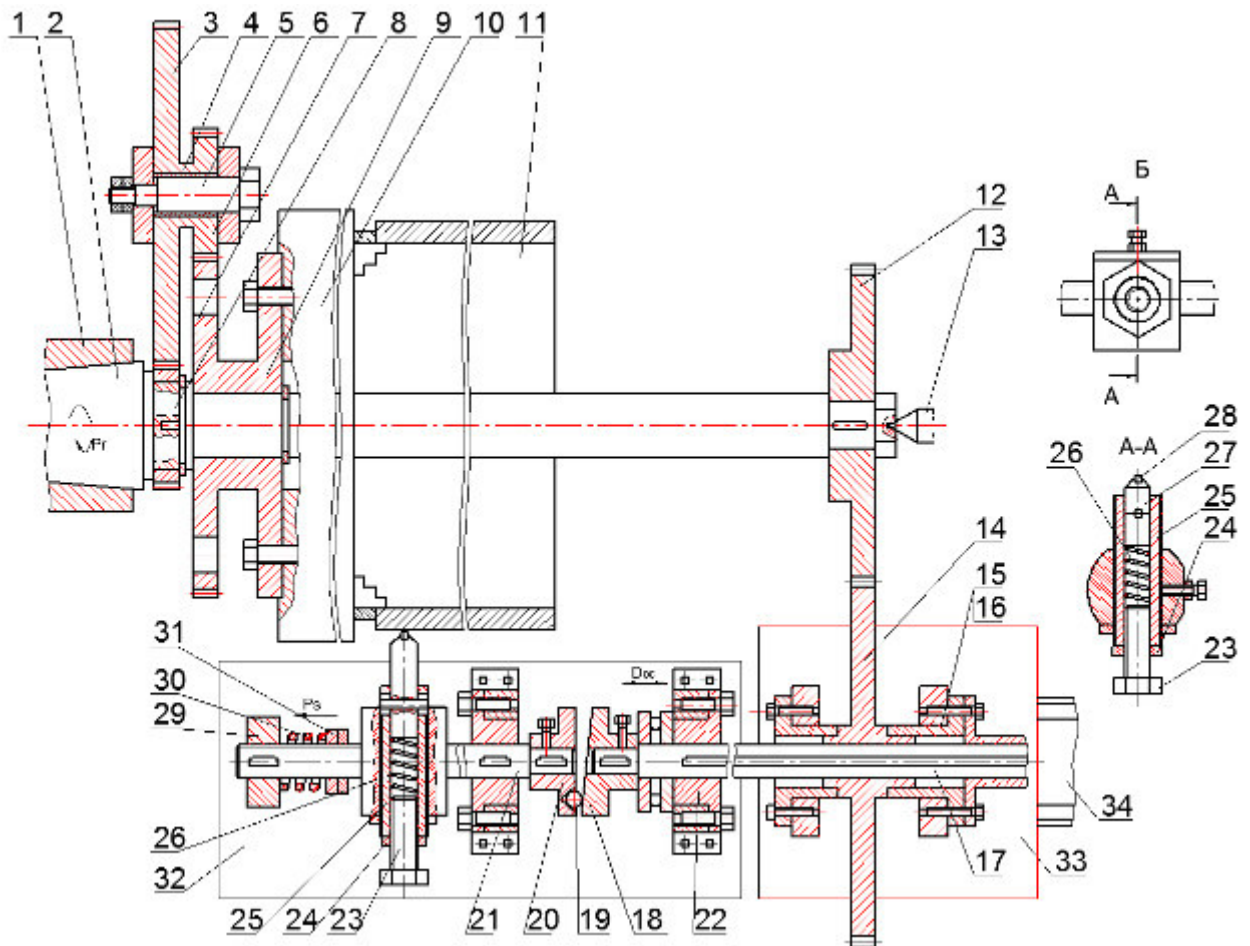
Пристрій для формування регулярного мікрорельєфу на зовнішніх циліндричних поверхнях в умовах дрібносерійного виробництва
